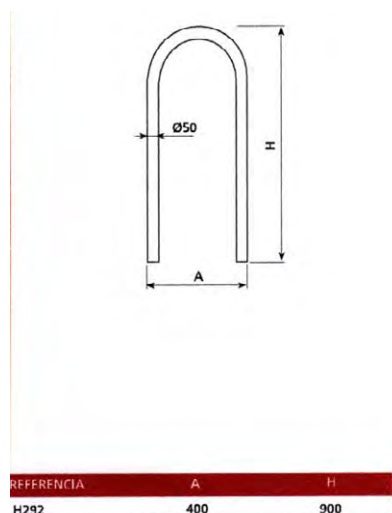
Dimensiones del Horquilla-protector de aceras elegido (fuente: www.benito.com).
